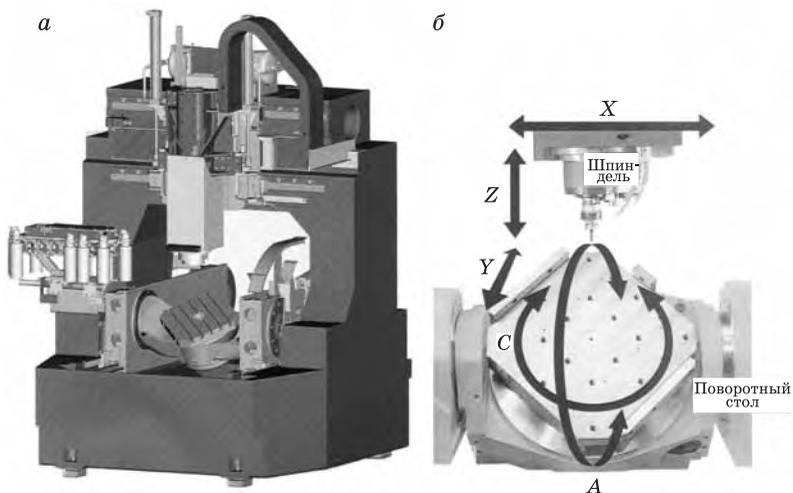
Многоцелевой сверлильно-фрезерно-расточной станок (а) и используемые оси координат (б)
